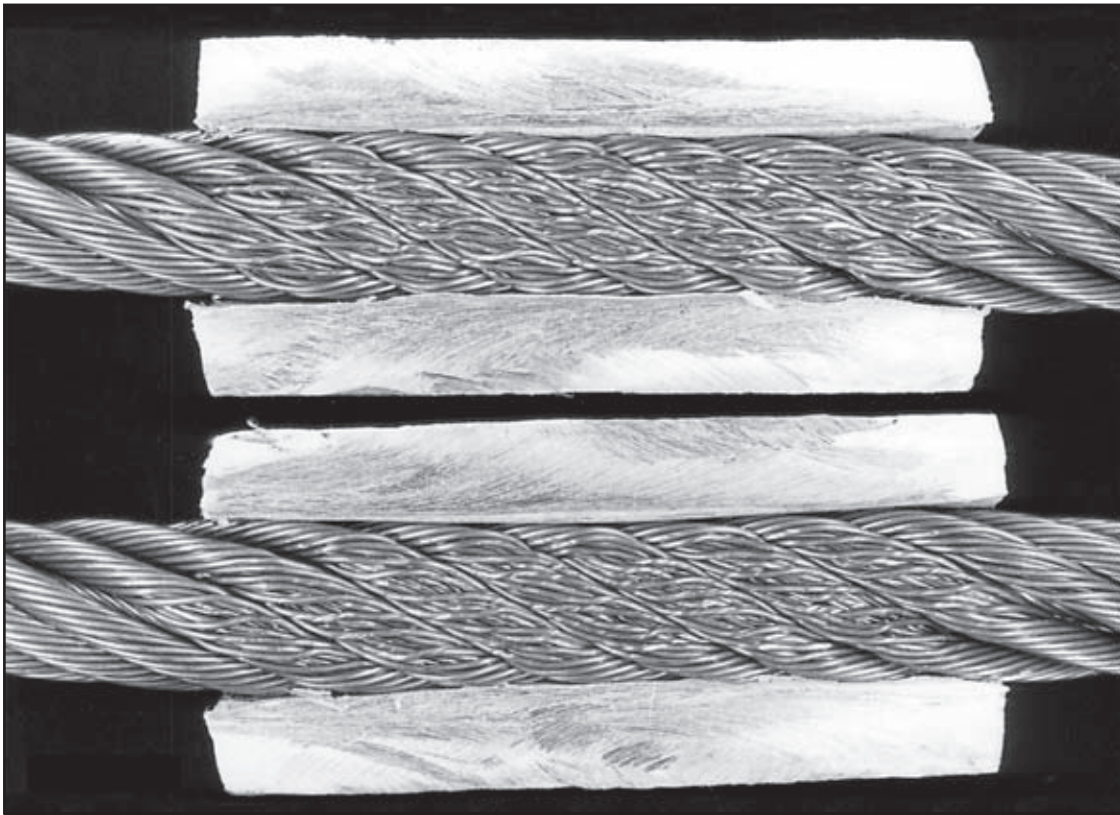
Aufgeschnittene Aluminiumklemmen mit Kreuzschlagseilen
